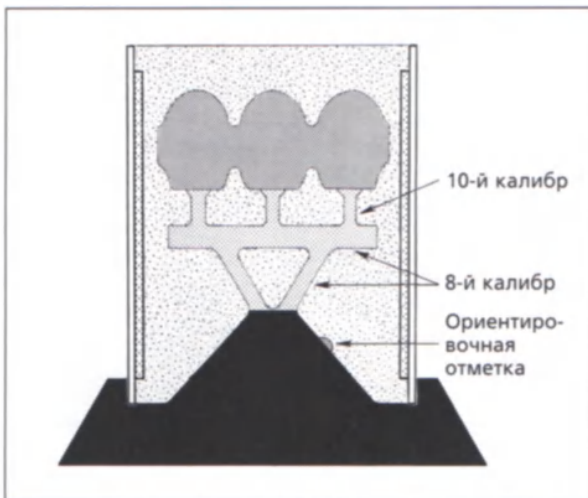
Для отливки каркаса металлокерамического НЧП создают непрямую литниковую систему. Для питающих литников и горизонтального коллектора используют литниковые штифты 8-го калибра и для отходящих от коллектора литников – штифты 10-го калибра
